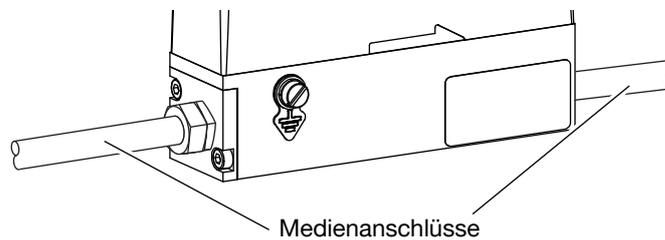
Medienanschlüsse, z. B. Innengewindeanschlüsse
